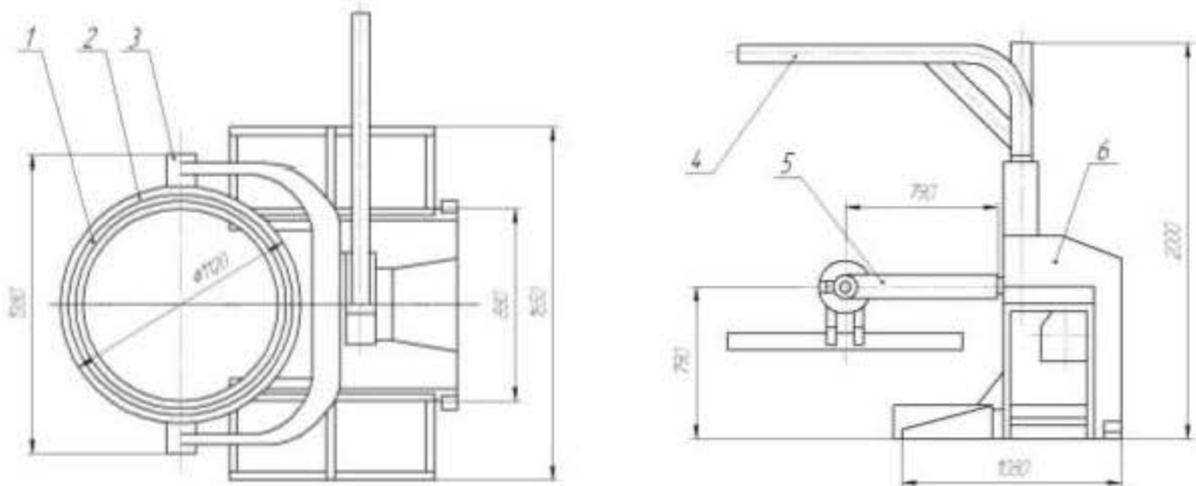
Стенд для разборки и сборки V- образных двигателей (Модель 6501-72)
